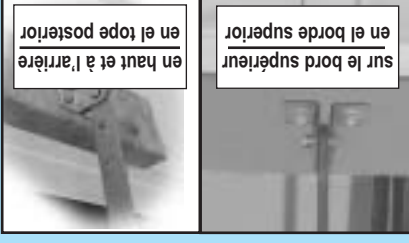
B Montage du support de porte. (monopiece) (monopieza). Montage de la cartela de la puerta.
